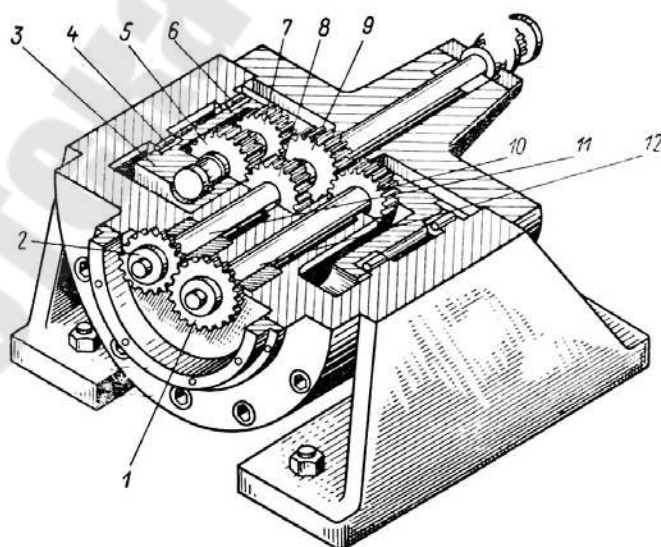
Стенд с перемещаемыми в окружном направлении отдельными зубчатыми колесами
